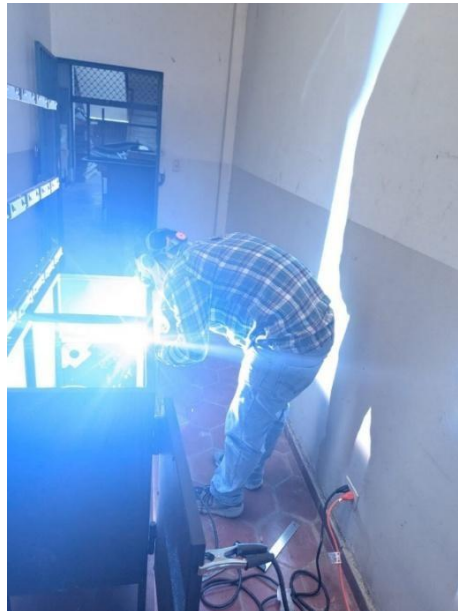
Construcción de repisa en la estructura principal. (Fuente: Autores).
